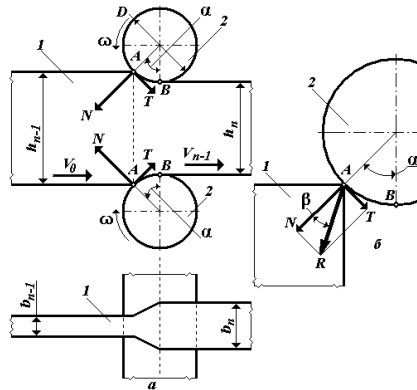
Схема продольной прокатки: а - установившийся процесс; б - силы, действующие на заготовку в момент захвата; 1 – заготовка; 2 – валок; N – нормальная сила; T – сила трения; R – равнодействующая сила; А-В – дуга захвата; α - угол захвата; β - угол трения; h_{n-1} , b_{n-1} – толщина и ширина заготовки; h_n , b_n – толщина и ширина изделия; D – диаметр валка
